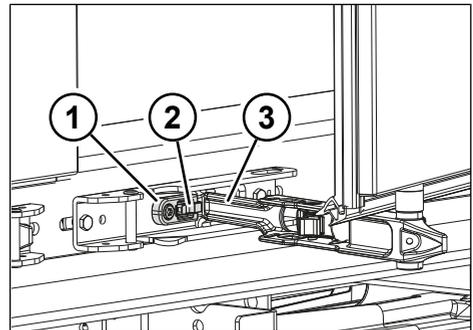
Leva per chiusura porte bloccata in posizione nel fissaporte
